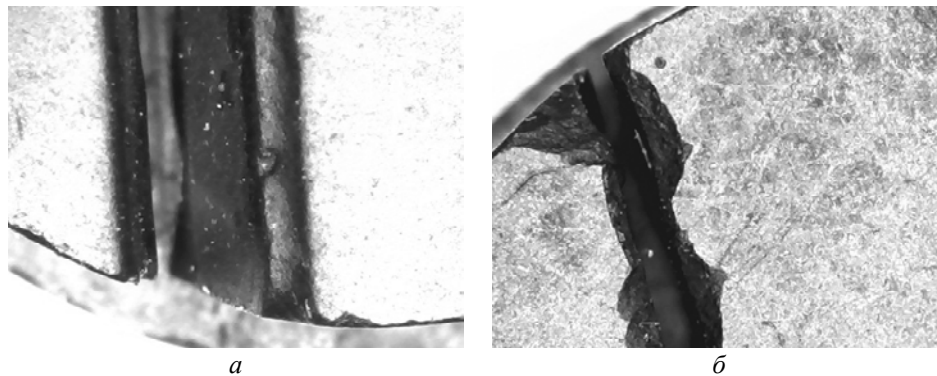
Рез на заготовке из ПСТМ с дефектом, вызванным начальным отклонением струи (*а*), сколы на торце заготовки на входе струи (*б*); $\times 50$.
